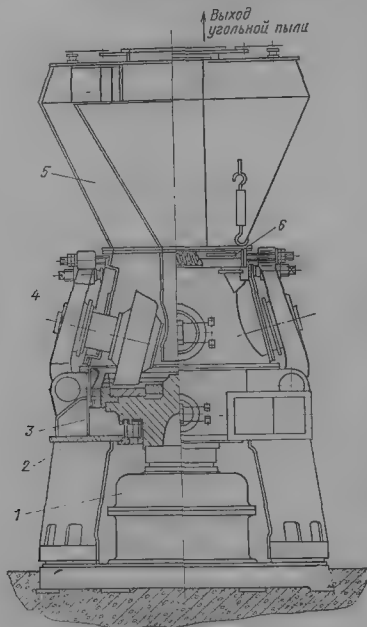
Общий вид валковой среднеходной мельницы:
